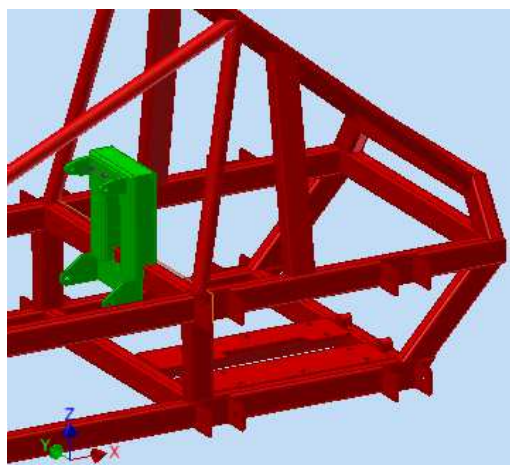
Umístění nosníku předních úchytů motoru na rámu
